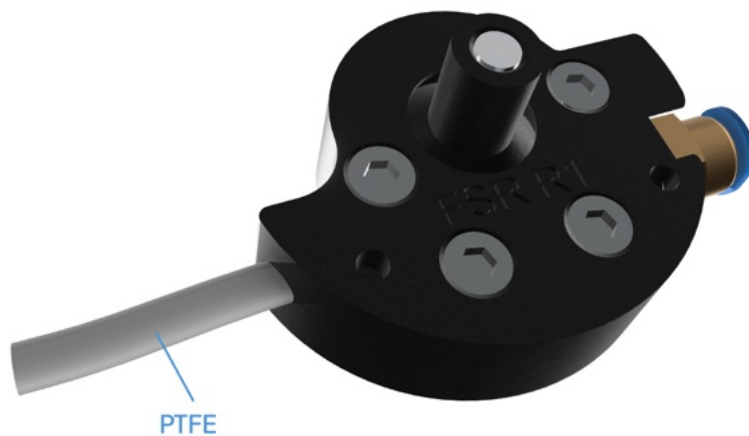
Rewinder-Chassis Montageschritt 18.
